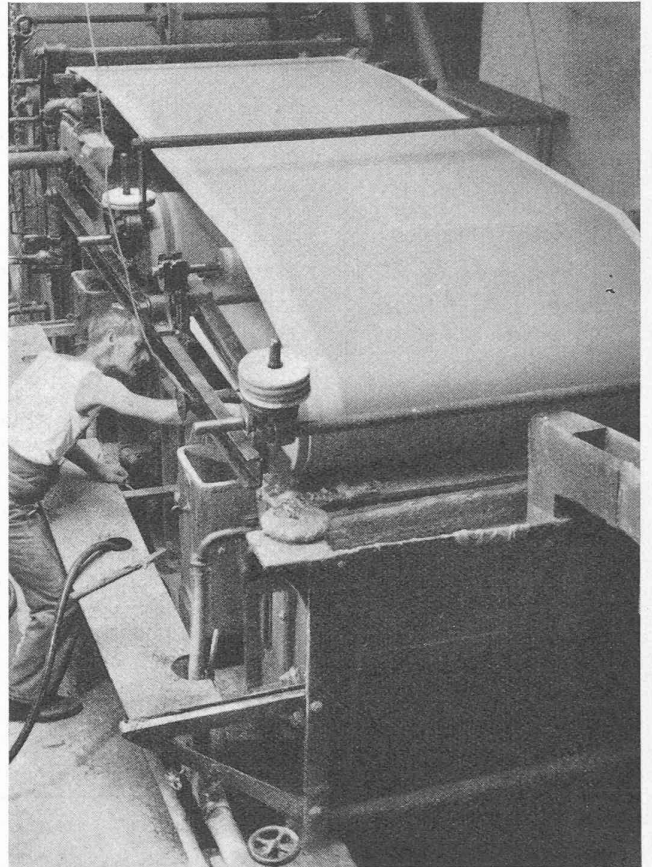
Machine à carton. — Contrôle du cylindre tamiseur.
